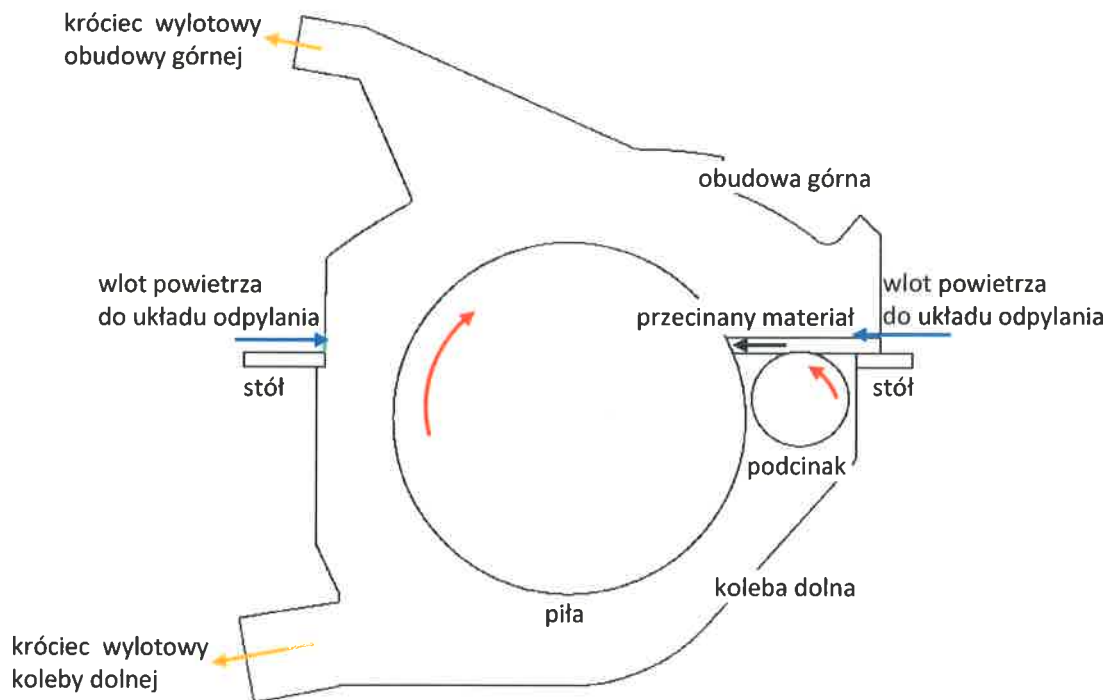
Przygotowany model numeryczny układu odpylania pilarki formatowej wraz z nożem rozdzielającym i warunkami brzegowymi (stan bazowy - średnica piły \varnothing 300 mm) (opracowanie własne)
